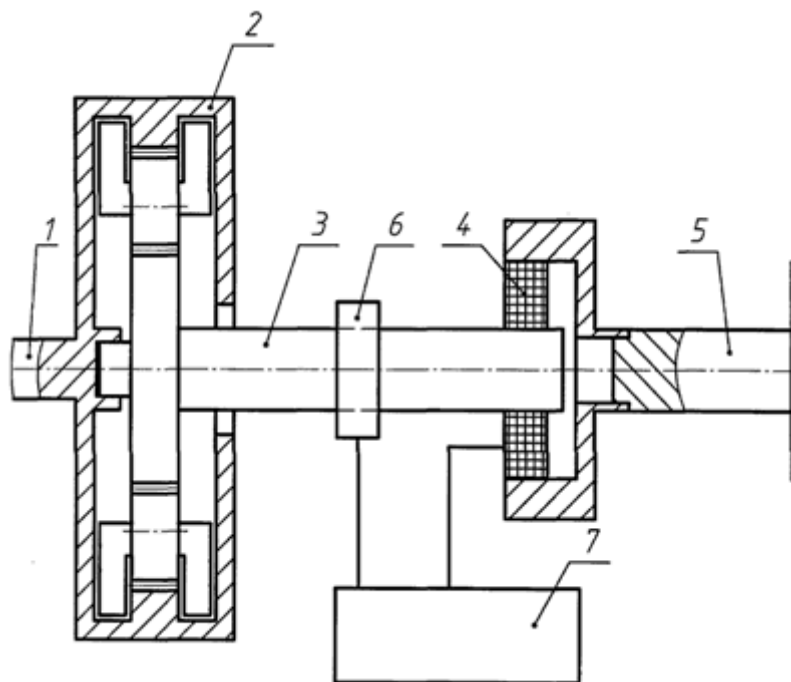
Схема инерционного устройства без корпусного механизма свободного хода
